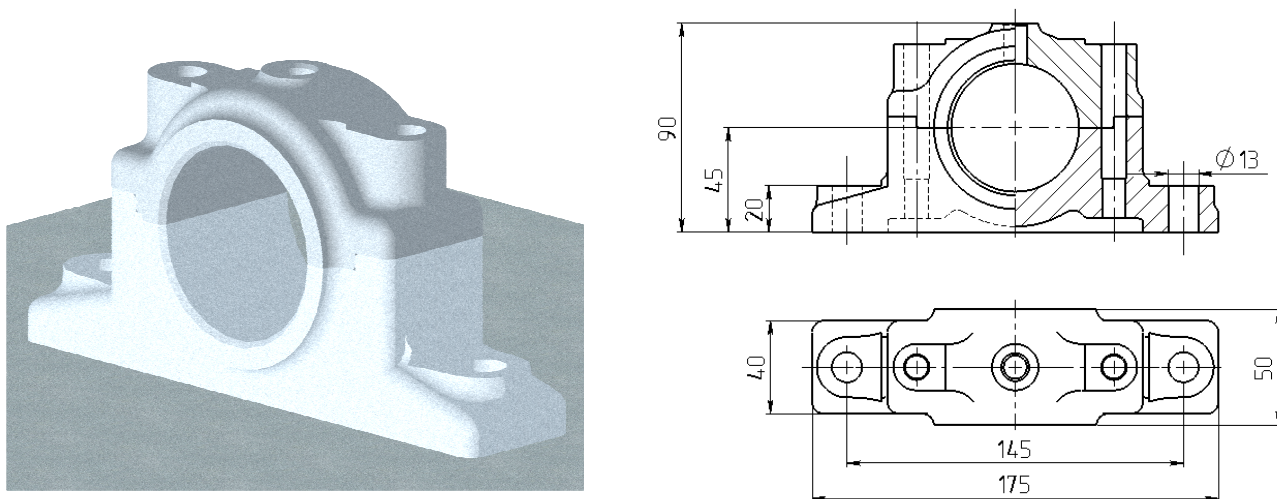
Корпус підшипника ковзання литий, роз'ємний, з двома кріпильними отворами
